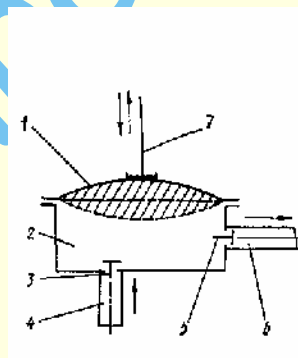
Диафрагменный насос с совмещенной клапанной коробкой
